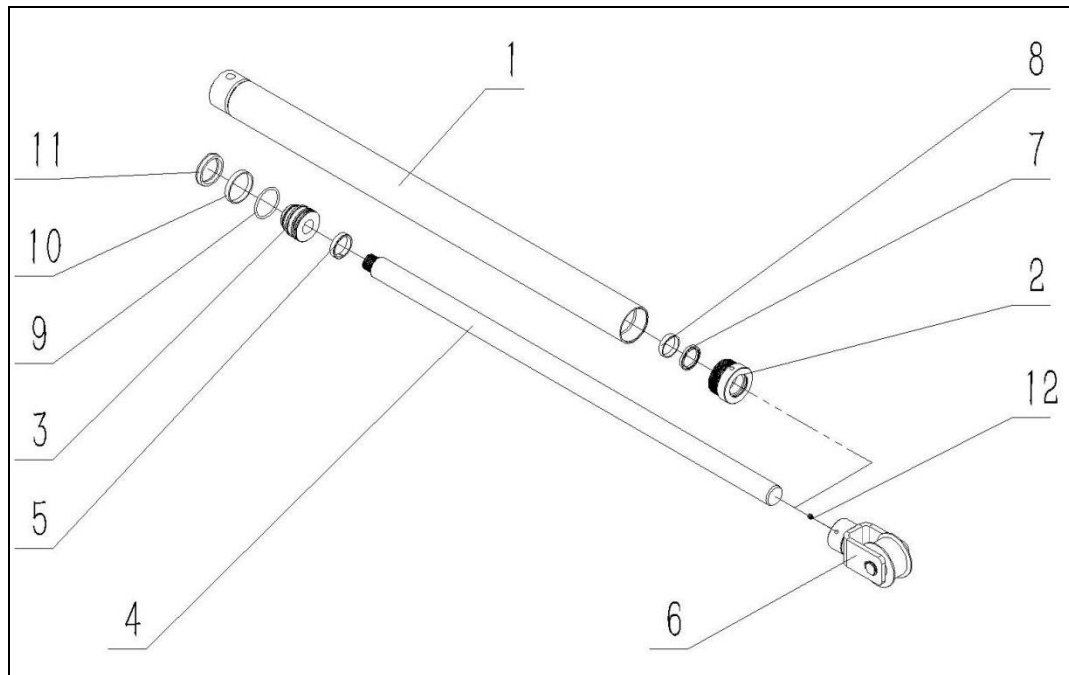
Explosionszeichnung des Hebebock-Zylinders
